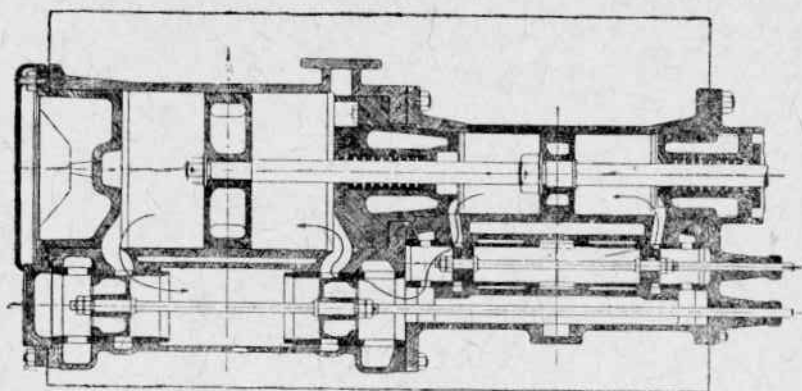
Продольный разрез по цилиндру локомотивной однокривошипной паровой машины двойного расширения.
